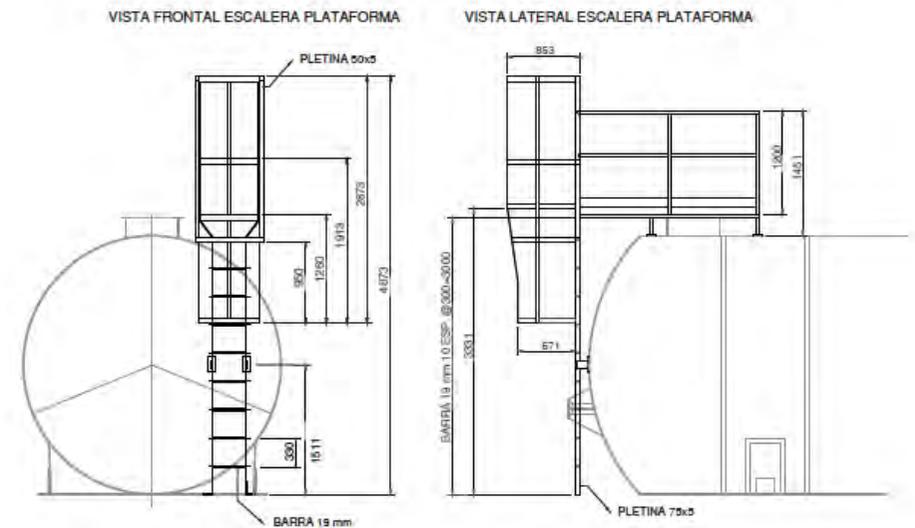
Vista Frontal y Lateral de Escalera. Fuente: Planimetría Ecova
